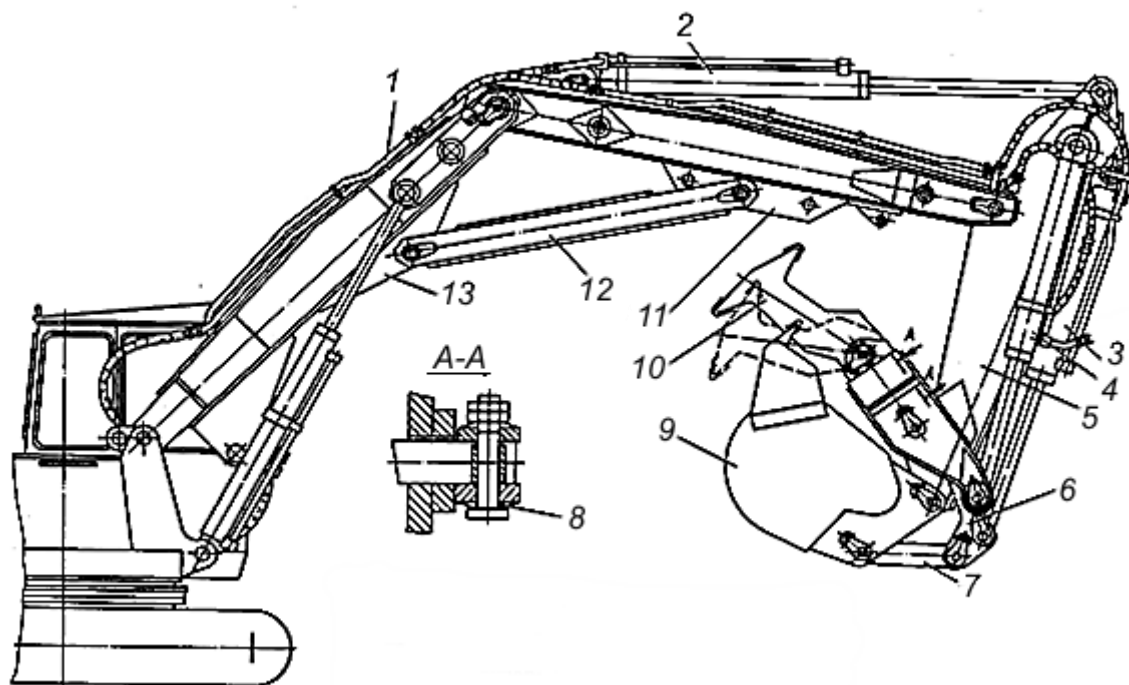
Рабочее оборудование захватно-клещевого типа с однозубым рыхлителем:
